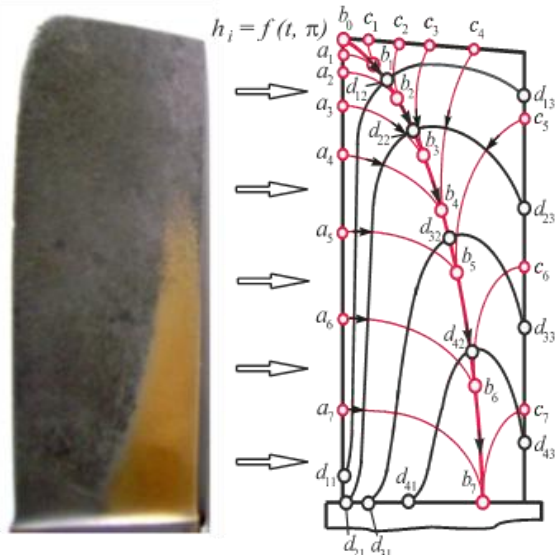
Схема закономерностей абразивно-эрозионного износа поверхности корытца пера лопатки компрессора вертолетного ГТД серии ТВ3-117
